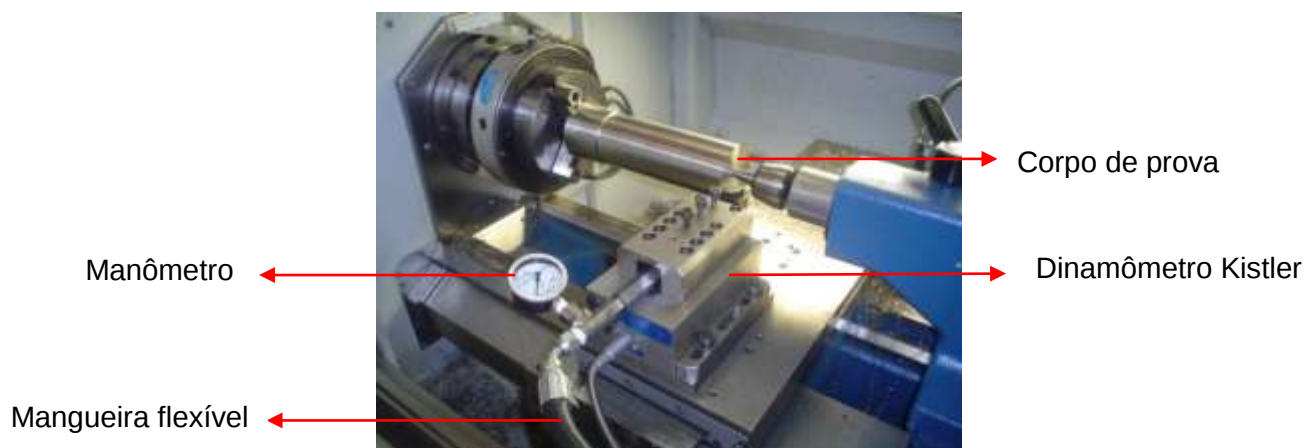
Torno CNC e componentes para aplicação de fluido de corte a alta pressão.
